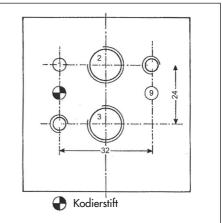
Anschlussbild gemäß VDI/VDE 3847
